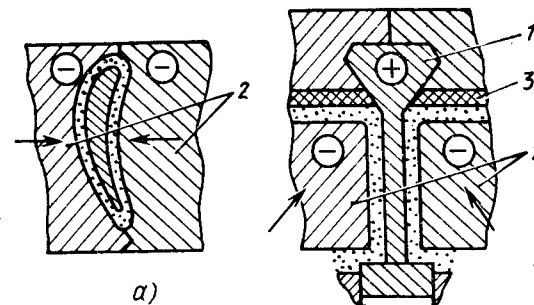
Схема круговой ЭХО пера лопатки компрессора:
